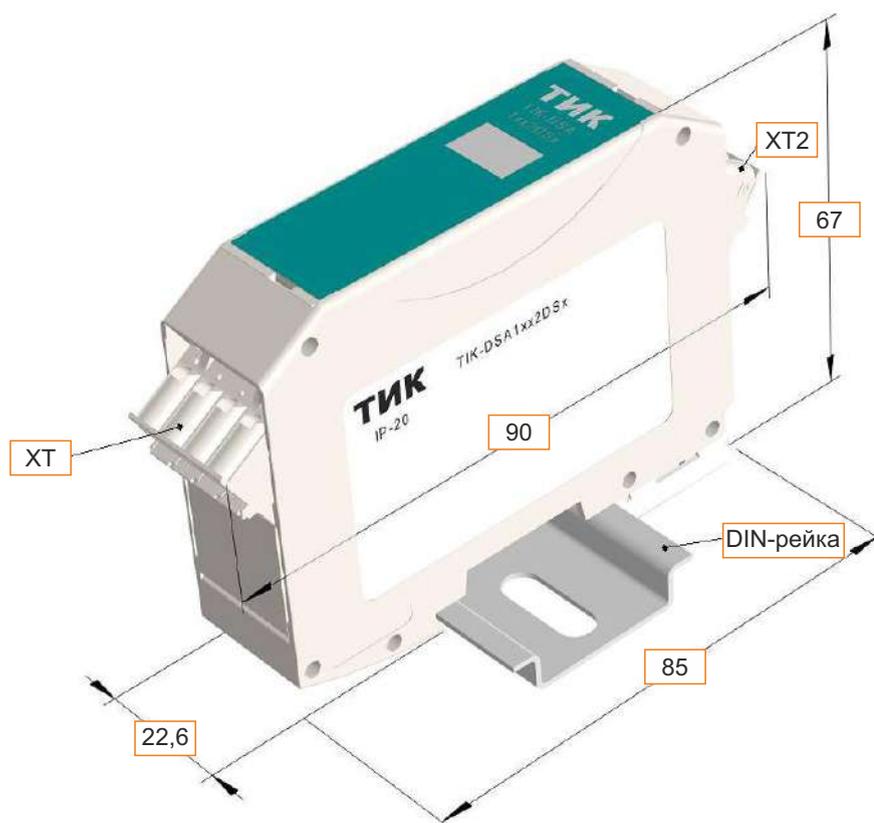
Пластиковый корпус на DIN-рейке (с индикацией)
